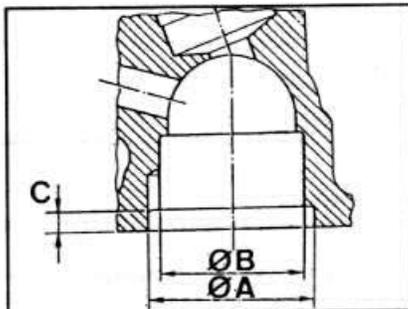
E.19. Размеры гнезда вихревой камеры сгорания в головке блока цилиндров.
